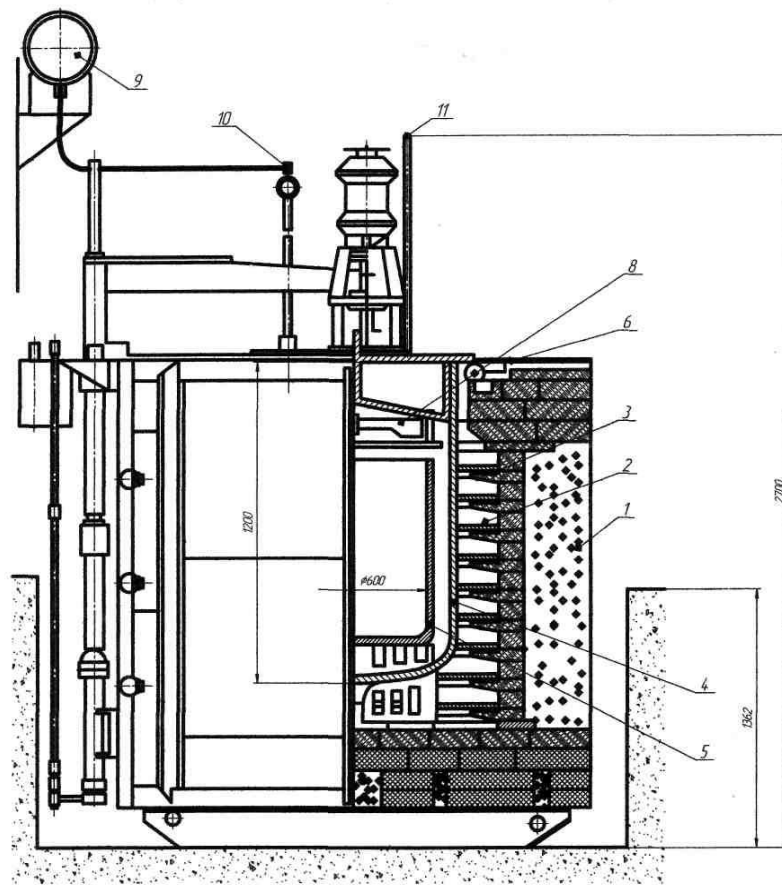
Шахтна муфельна цементаційна піч СШЦМ - 6.12/9: 1 - металевий каркас; 2 - нагрівальна камера; 3 - нагрівальний елемент; 4 - жаротривка реторта; 5 - кошик для деталей; 6 - кришка; 7 - гідравлічний механізм; 8 - вентилятор; 9 - бачок для рідини; 10 - кран регулювальний; 11 - отвір для відпрацьованого газу.
